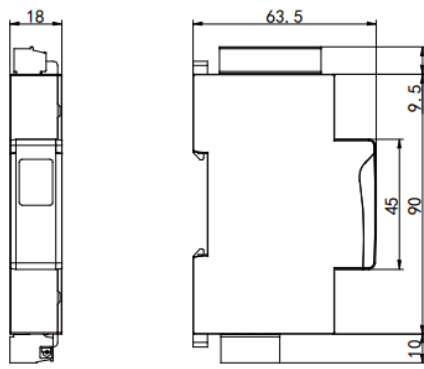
Внешний вид и габаритные размеры модуля измерительного КСМ-М3
